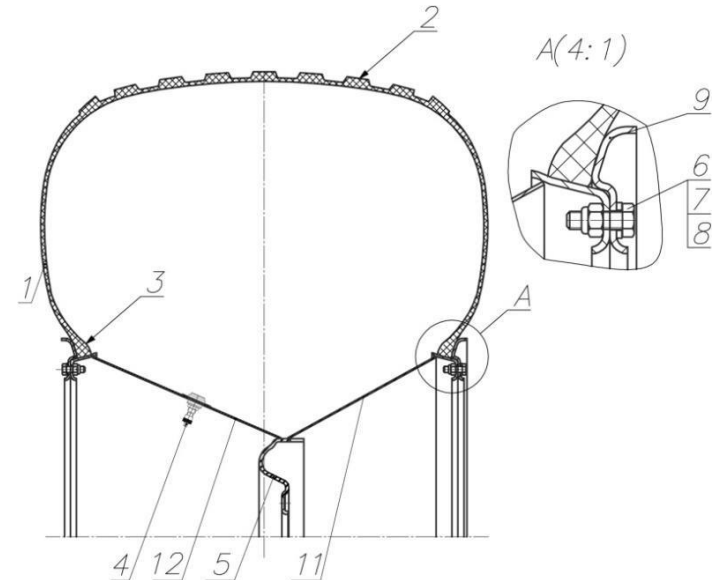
Шина 1300x600-533 ТРЭКОЛ с колесом в сборе
